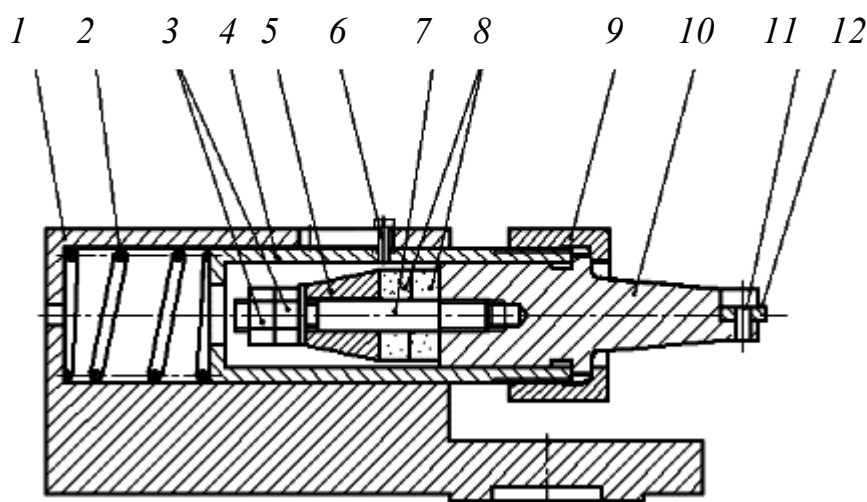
Устройство для твердосплавного выглаживания заготовок с наложением УЗК: 1 – корпус; 2 – пружина; 3, 9 – гайка; 4 – стакан; 5 – отражающая шайба; 6 – винт; 7 – шпилька; 8 – пьезокерамические кольца; 10 – волновод; 11 – штифт; 12 – деформирующий элемент (индентор)
